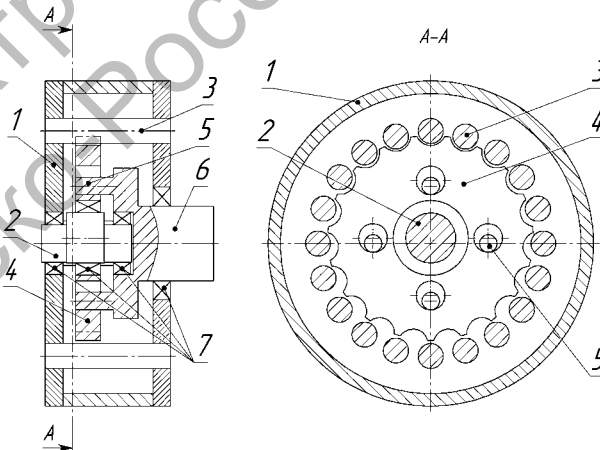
Конструктивная схема планетарной эксцентриковой передачи: 1 – корпус; 2 – вал эксцентриковый; 3 – ролики корпуса; 4 – сателлит; 5 – механизм параллельных кривошипов; 6 – вал выходной; 7 – опорные подшипники
